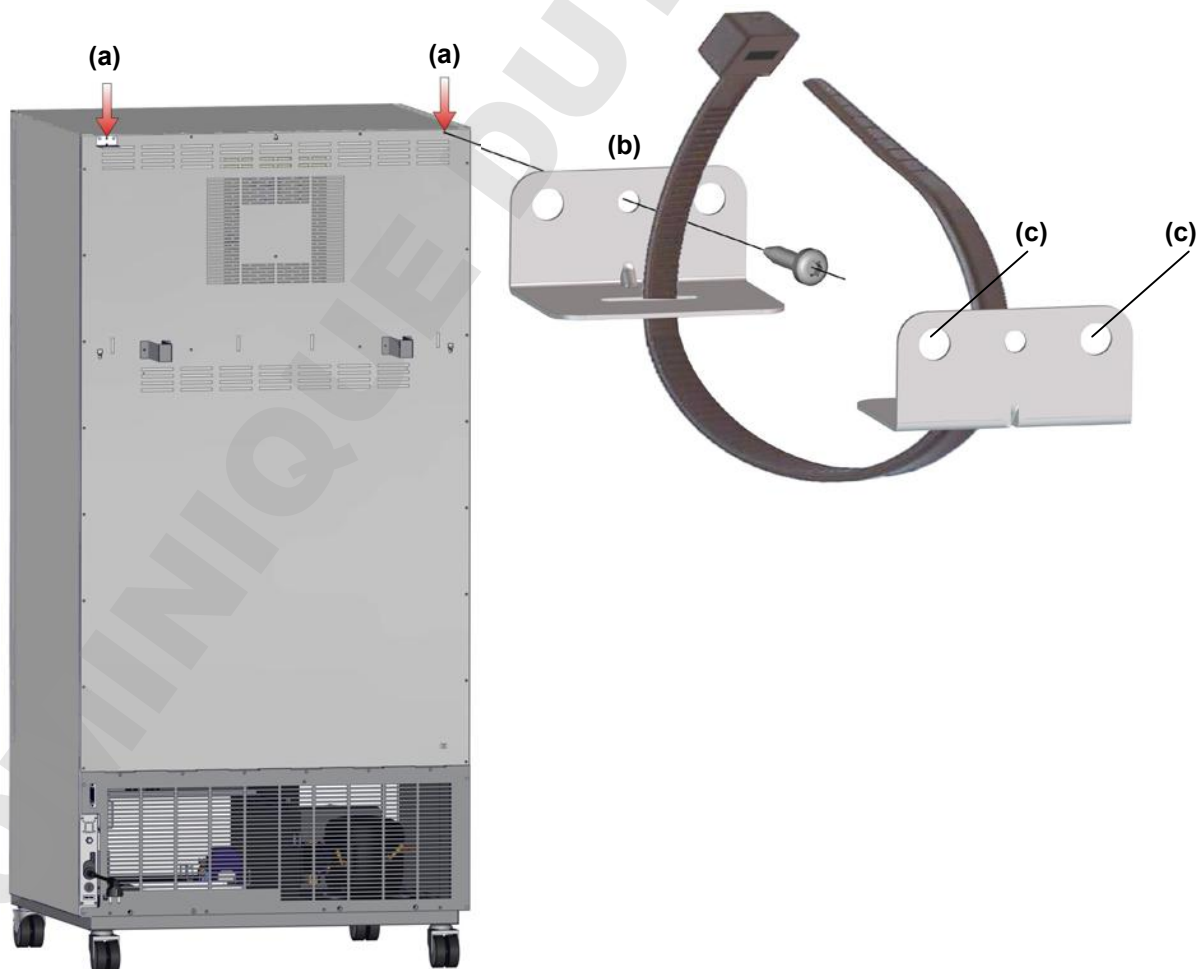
Retro KBW 400 ed installazione della protezione antiribaltamento
